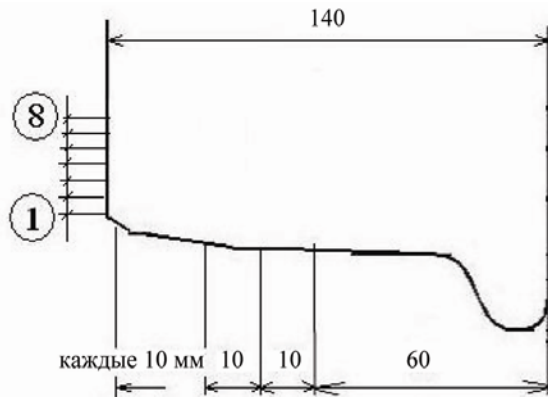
Схема вимірювання твердості бокової поверхні колеса:
